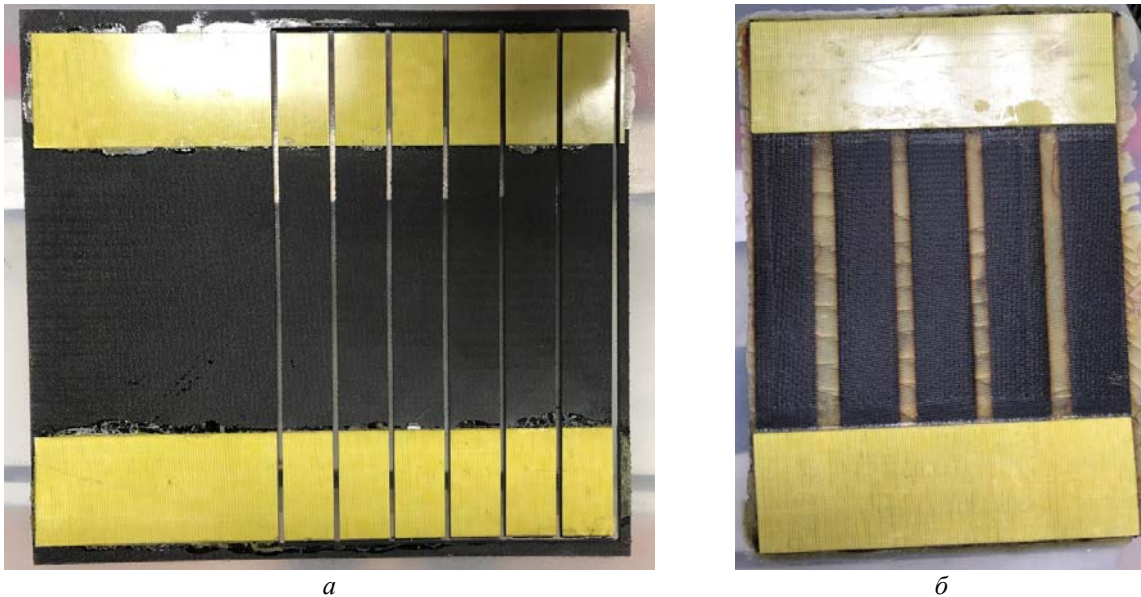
Образцы для испытаний, изготовленные методом TFR:
